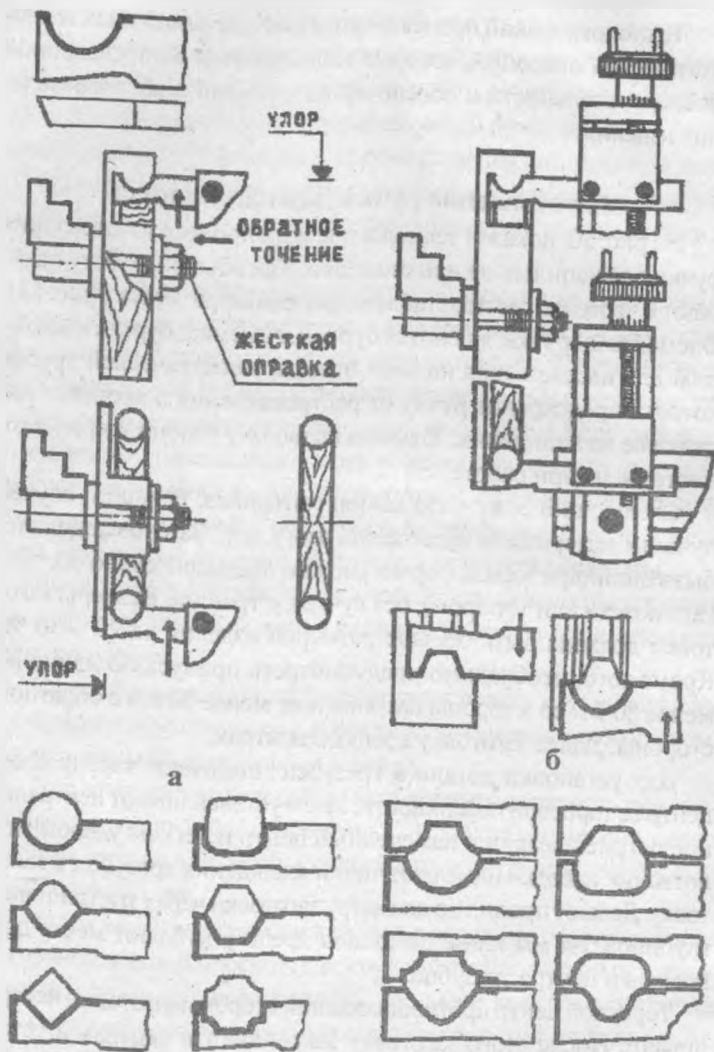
Точение колец и построение профиля кольца одним и двумя резцами
